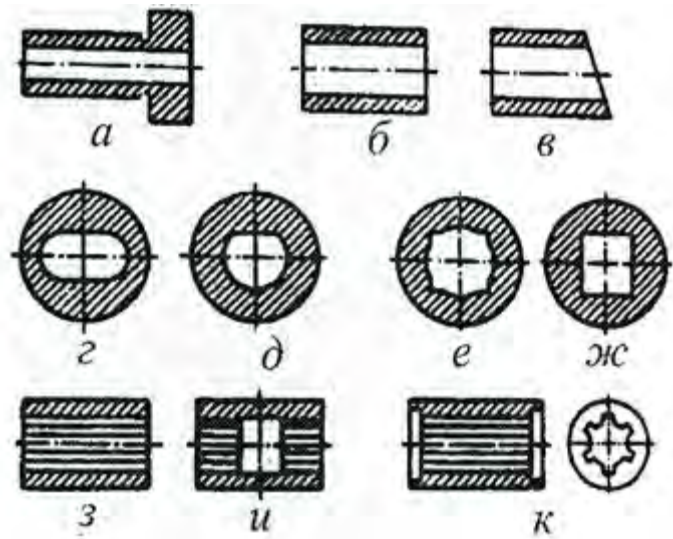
Приклади конструкцій деталей машин, оброблюваних на протяжних верстатах
